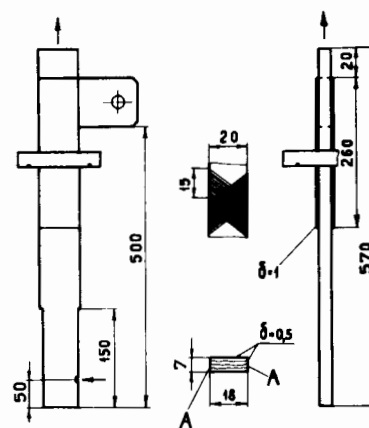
Токоввод на 1,6 кА, А - место сварки.
